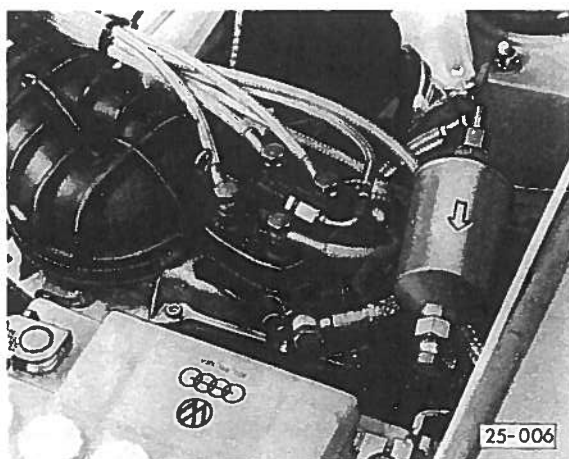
Position de montage du filtre à carburant: la flèche indique le sens d'écoulement
